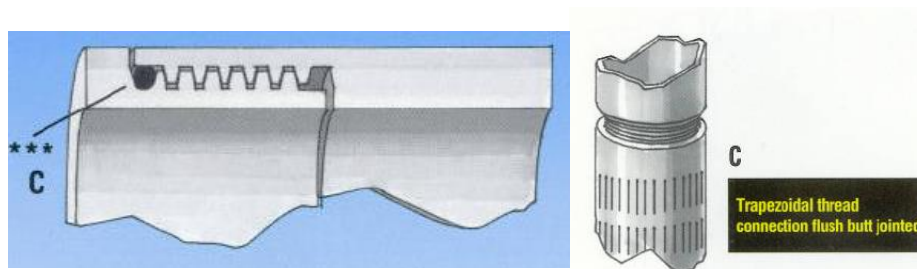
Tipo de conexão entre tubos e tipo de rosca.
